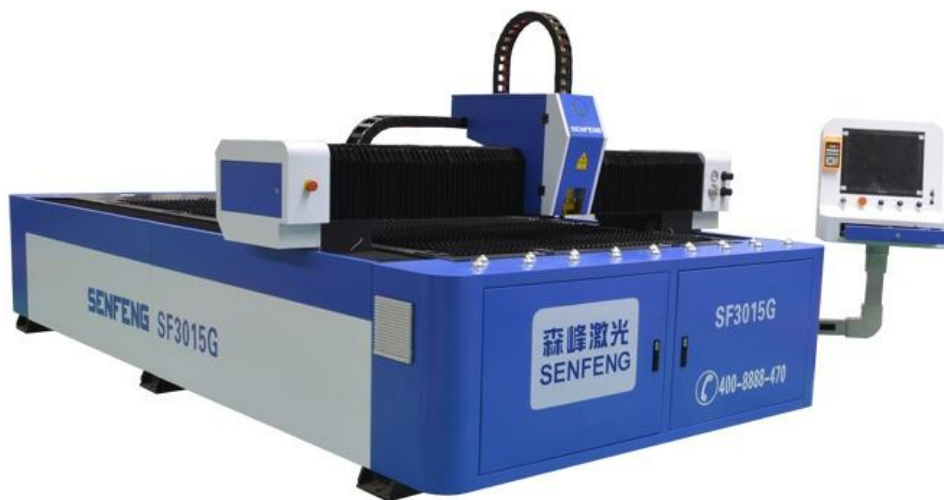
Оптоволоконний лазерний станок з ЧПК
